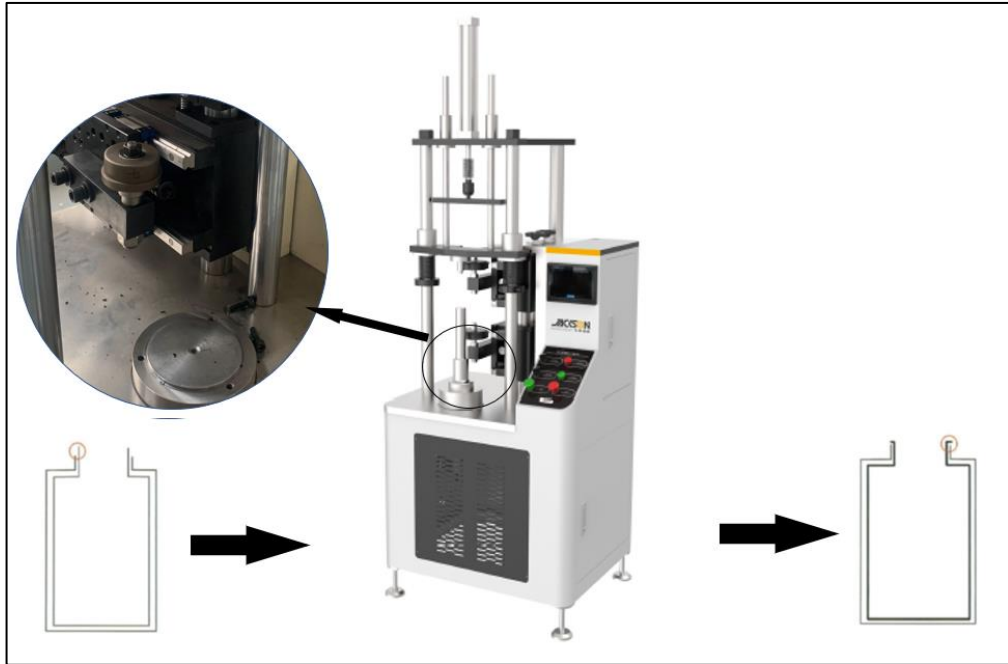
Alt Şekillendirme Makinesi (Proses – IV)
